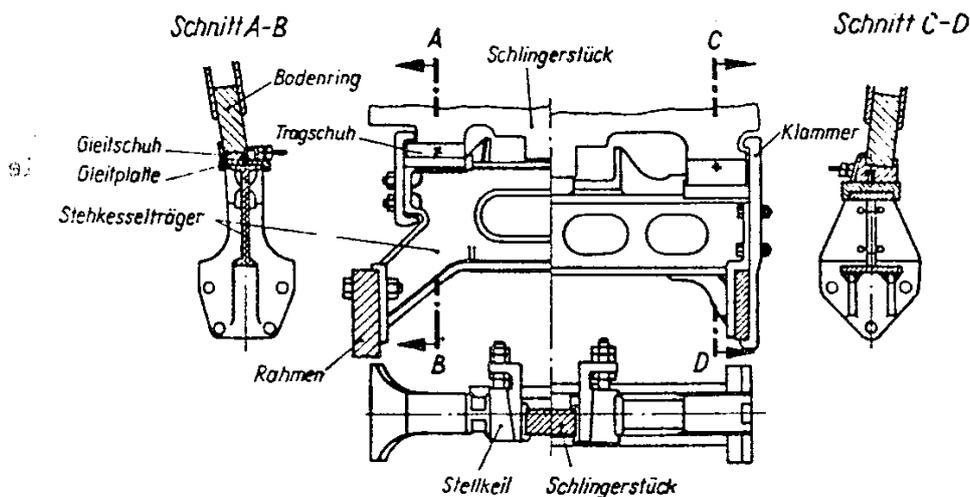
Stehkesselträger für untere Auflagerungen mit Schlingerstück
